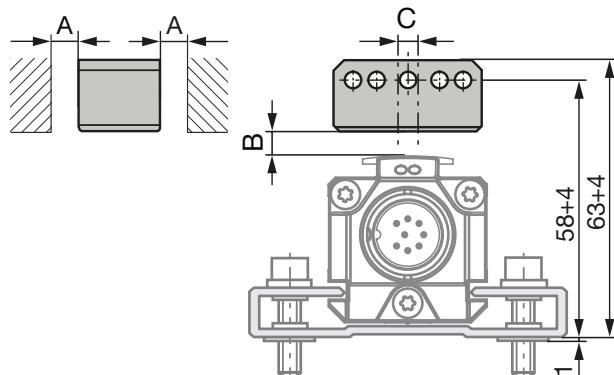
Dimensions et distances pour le capteur de position BTL6-A-3801-2
